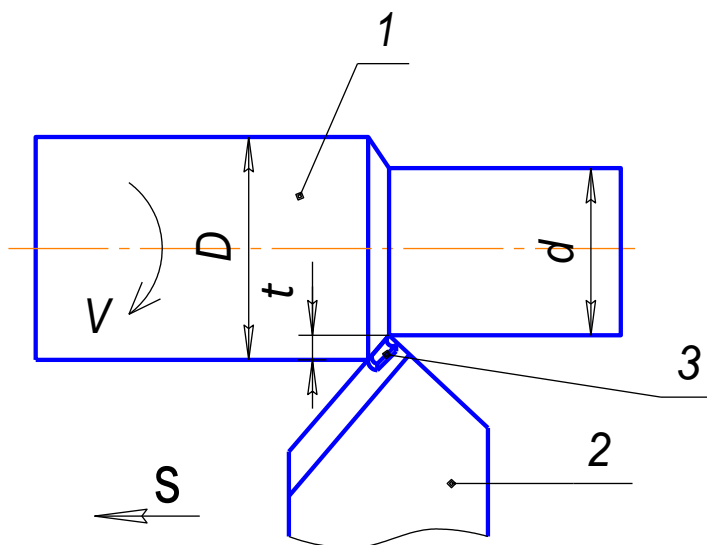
Процесс точения наружной цилиндрической поверхности: 1-обрабатываемая заготовка; 2-токарный резец; 3- стружка
